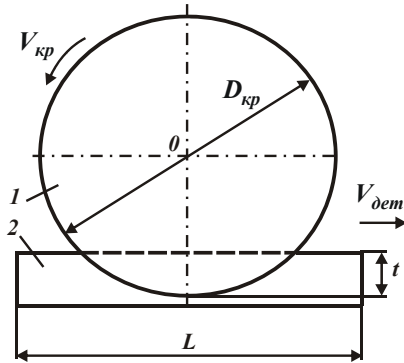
Расчетная схема шероховатости на боковой поверхности зуба колеса при шлифовании торцом круга: 1 – круг; 2 – зуб колеса
